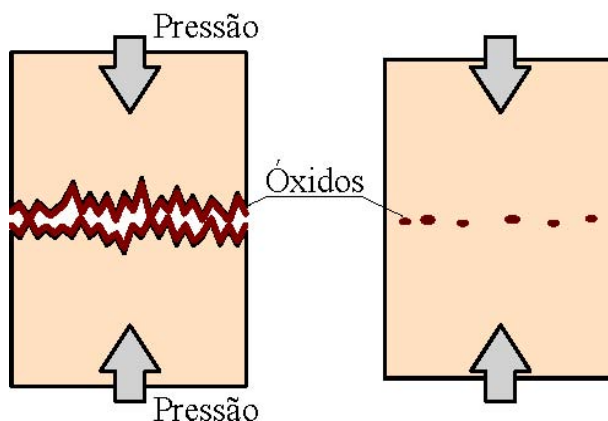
Soldagem por pressão ou deformação (Modenesi e Marques, 2006).
